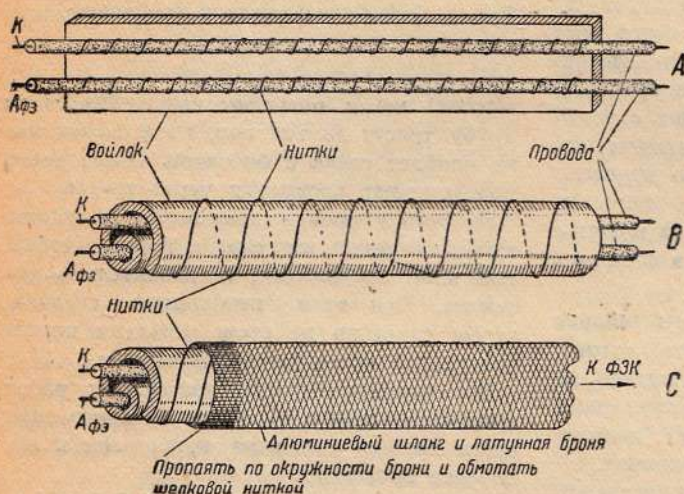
Устройство гибкого шланга фотоэлемента: А — заготовка, В — рулон, С — готовый гибкий шланг
